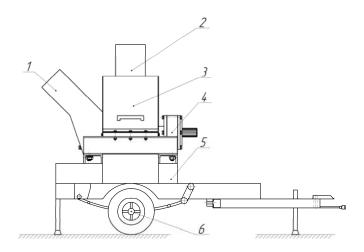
Мобильная многорезцовая рубительная машина: I — загрузочный патрубок; 2 — патрубок отвода щепы; 3 — ограждение маховика; 4 — опора подшипника; 5 — сварная рама; 6 — коленная пара
